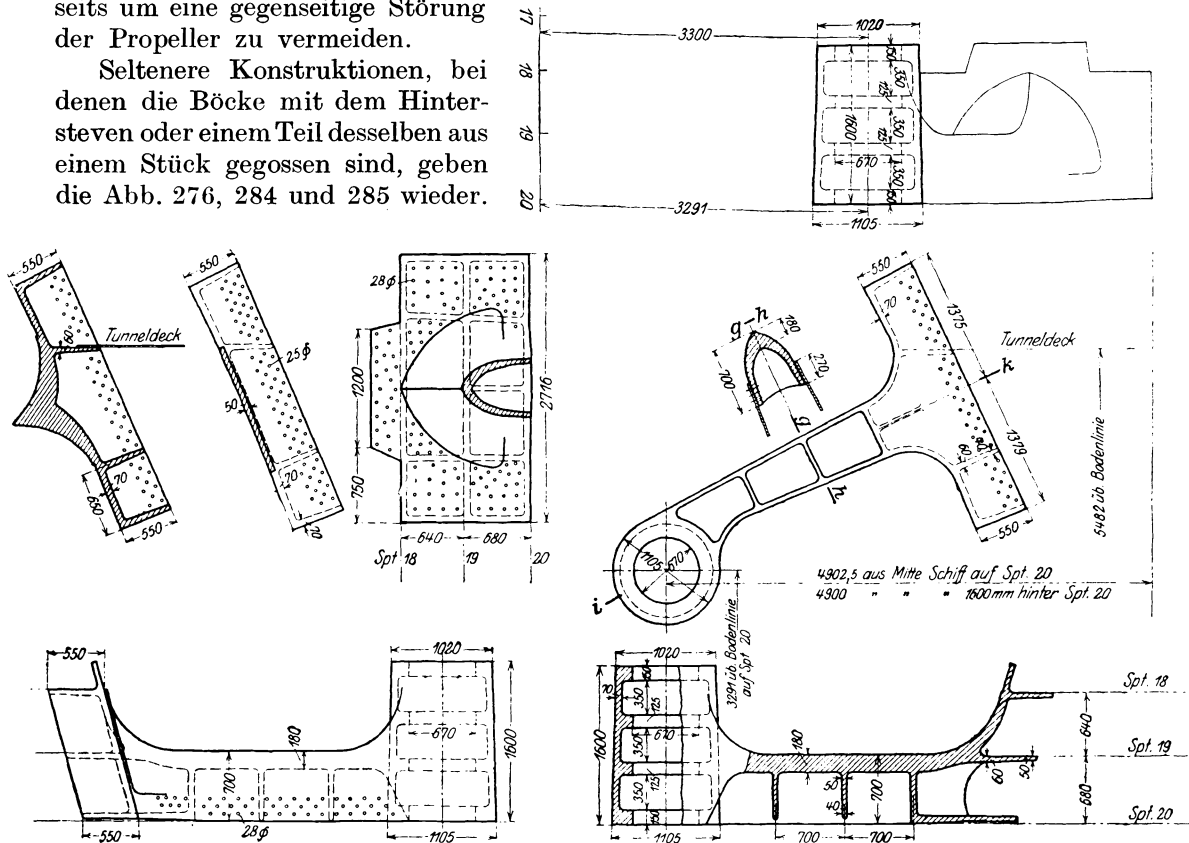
Wellenböcke des Dreischraubendampfers „Cap Polonio“.
